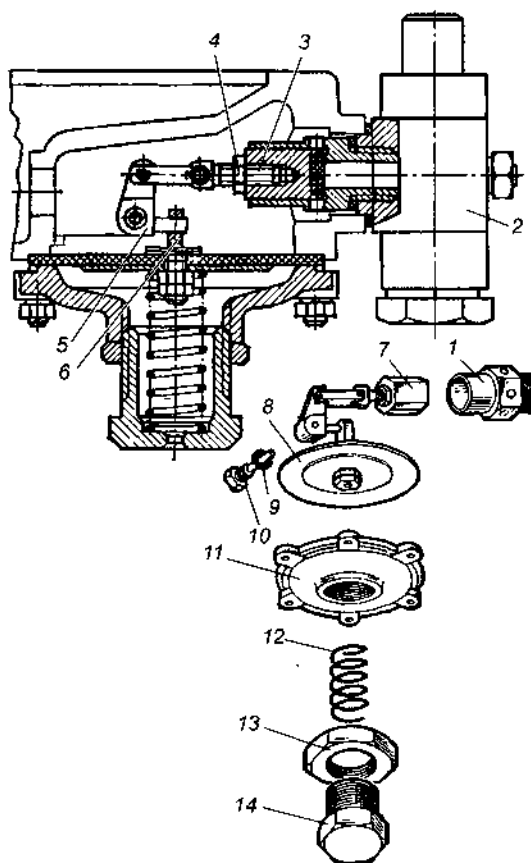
Первая ступень редуктора (в сборе) и ее детали: 1 — седло клапана; 2 — фильтр; 3 — регулировочный винт; 4, 13 — контргайки; 5 — рычажок; 6 — шток; 7 — клапан в сборе; 8 — мембрана в сборе; 9 — прокладка; 10 — ось рычажка; 11 — крышка; 12 — пружина; 14 — седло пружины (регулирующий болт)
